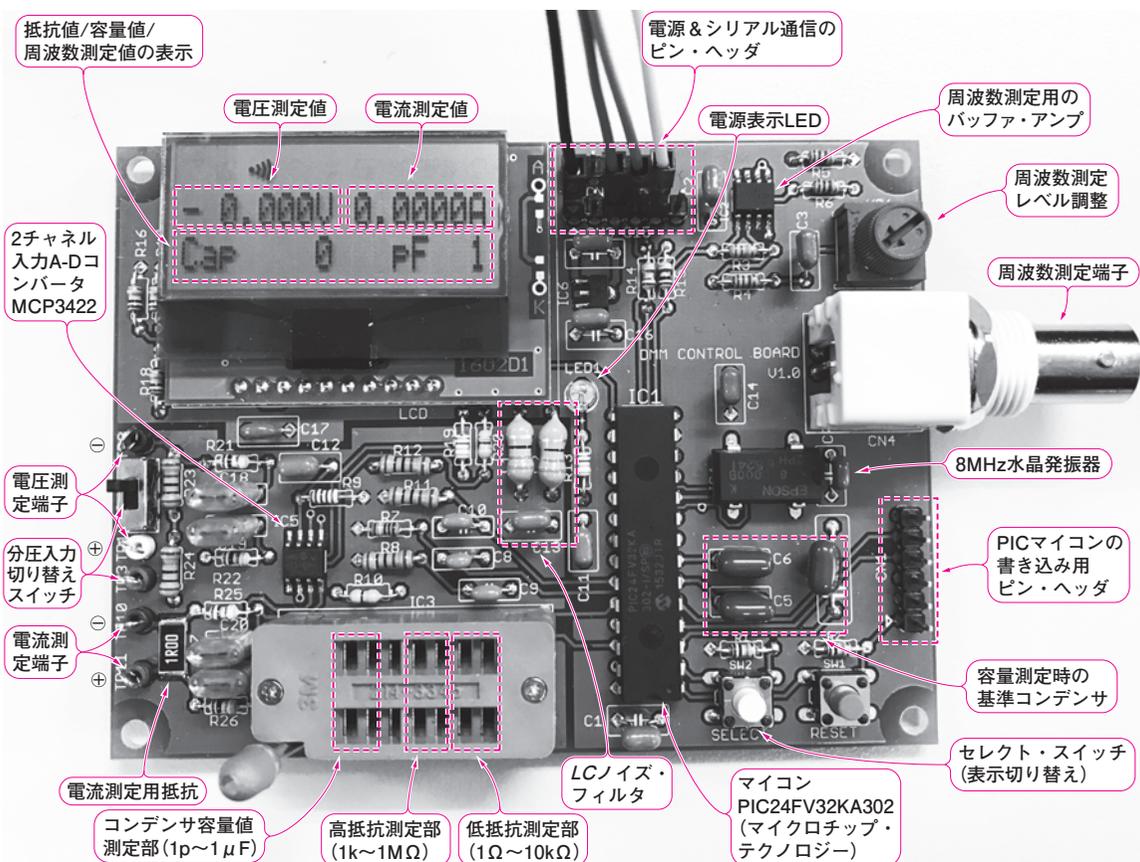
付録基板で作ったシリアル出力アナログ計測基板①「トラ技デジタル」(設計:後閑 哲也, 製造・販売:ビット・トレード・ワン)本誌の付録基板で製作できる。搭載用の部品一式をビット・トレード・ワンほかで購入できる。Linuxパソコン「ラズベリー・パイ」と組み合わせるとWi-Fi対応のビジュアル測定器が作れる。Windows用のソフトもある
